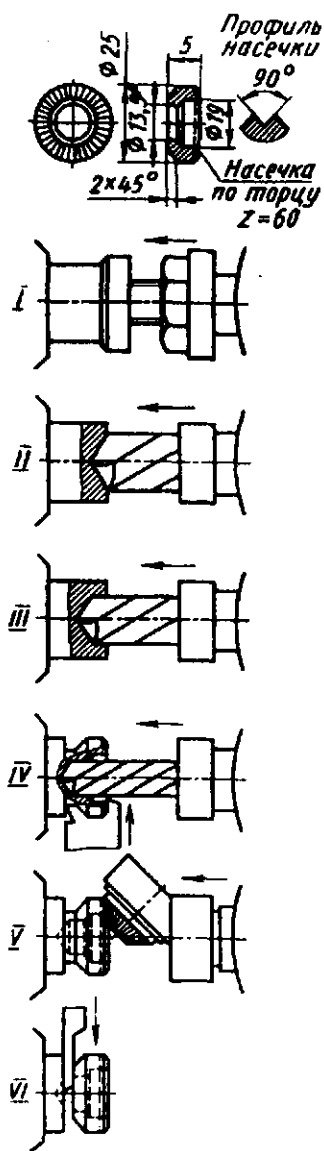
Наладка одношпиндельного токарно-револьверного автомата для обработки детали с насечкой по торцу
